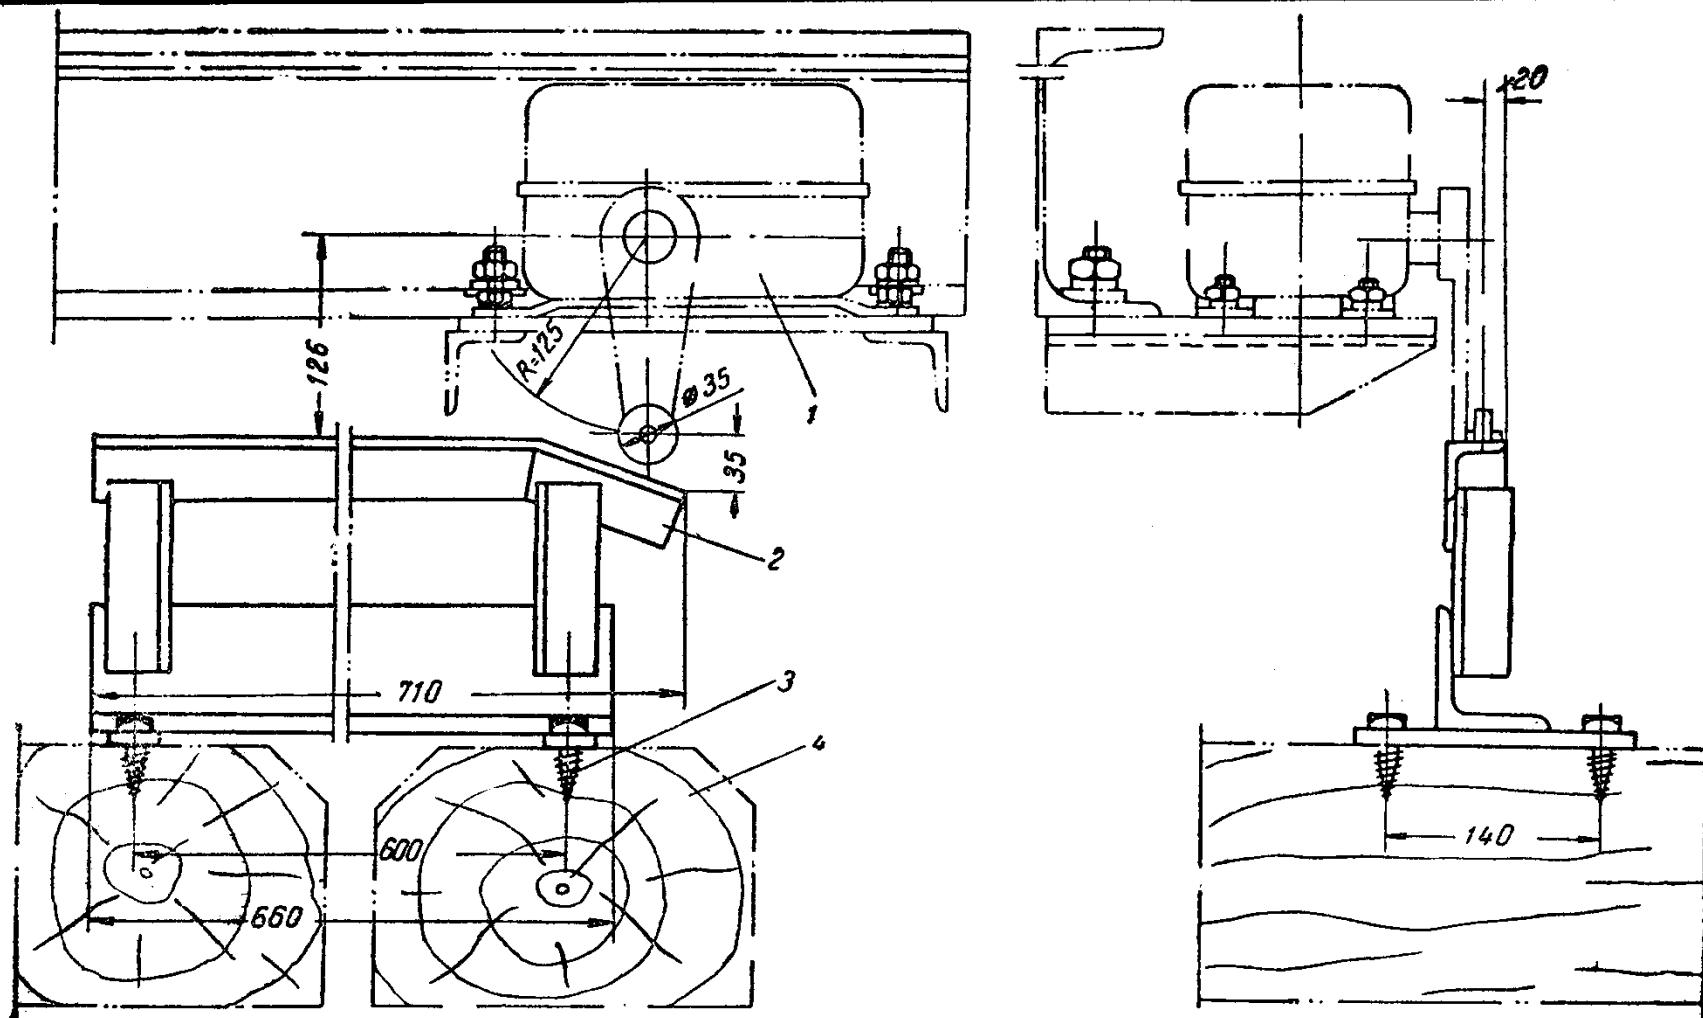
Схема установки упора конечного выключателя механизма передвижения
